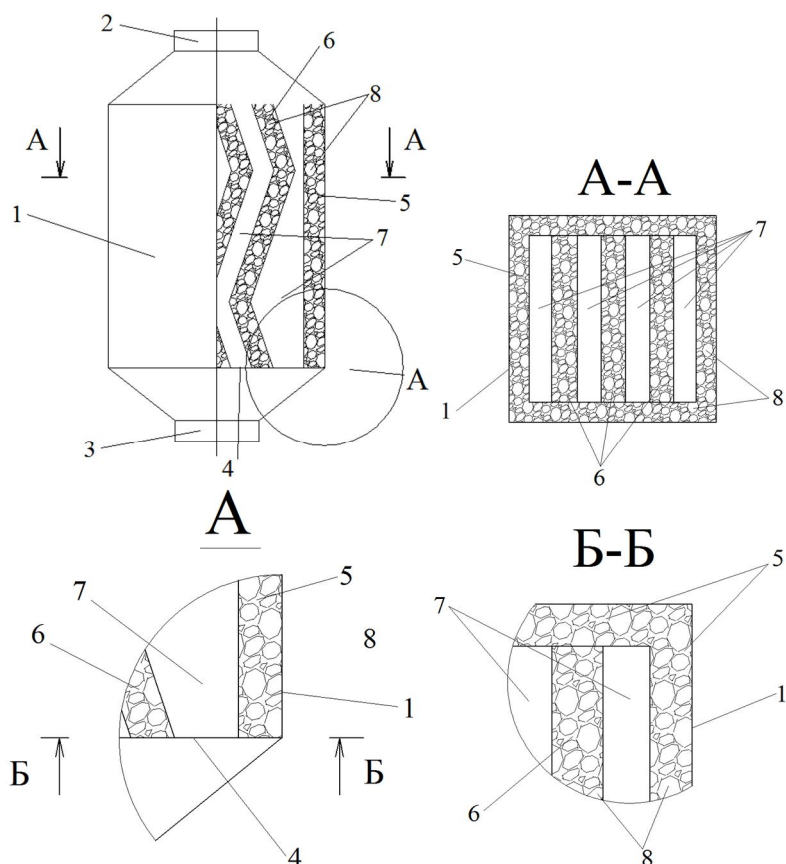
Насадка на дымовую трубу: 1 – корпус; 2 – верхний стыковочный узел; 3 – нижний стыковочный узел; 4 – перфорированная решетка; 5 – перфорированные вертикальные кассеты; 6 – перфорированные зигзагообразные кассеты; 7 – восходящие газовые каналы; 8 – доменный гранулированный шлак
